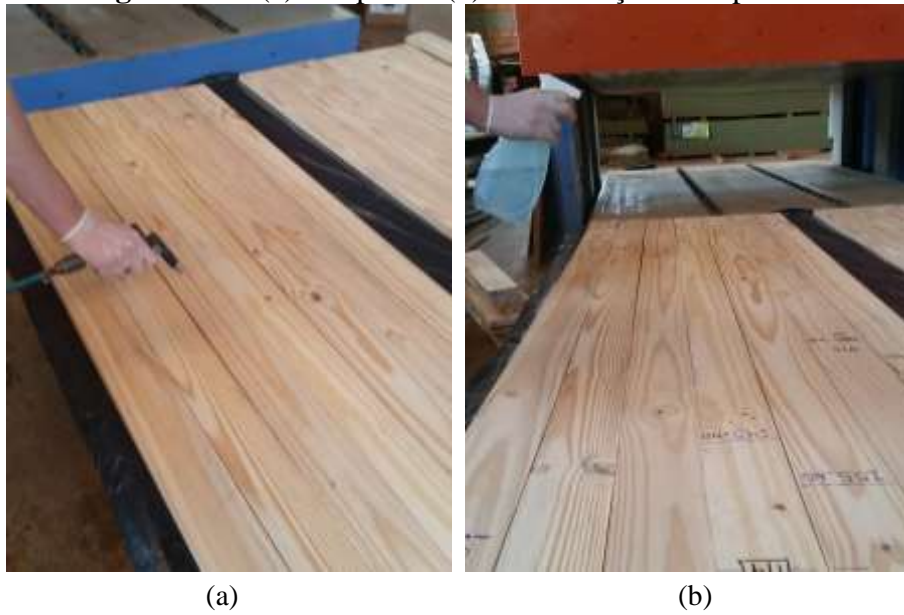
(a) Aplicação do adesivo e (b) disposição das lamelas da camada adjacente
